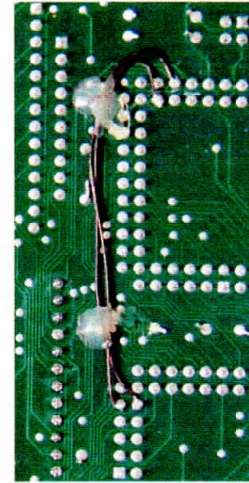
Detalle de interruptor S2 de la tarjeta Power Distribution Board Assembly.
